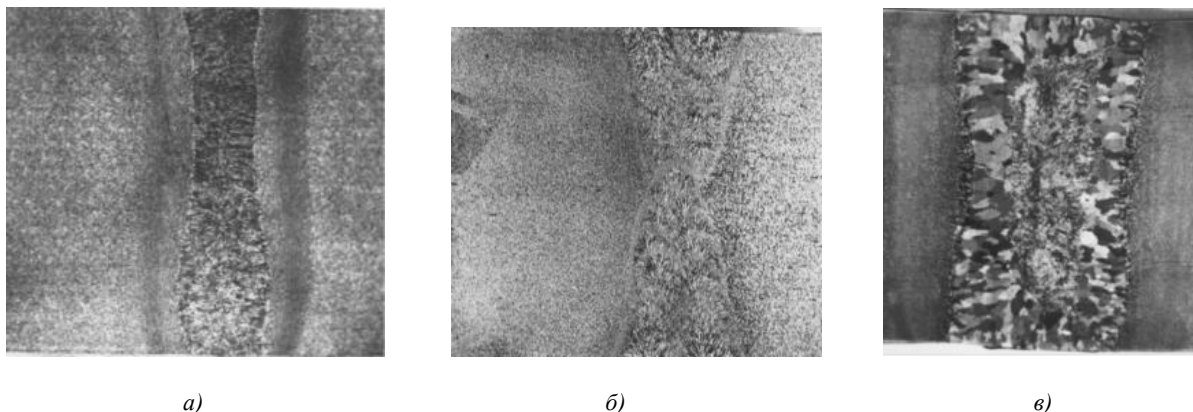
Макростроение сварного соединения, выполненного способом: а — сварки в щелевую разделку; б — автоматической сварки под флюсом; в — ЭШС, $\times 100$
